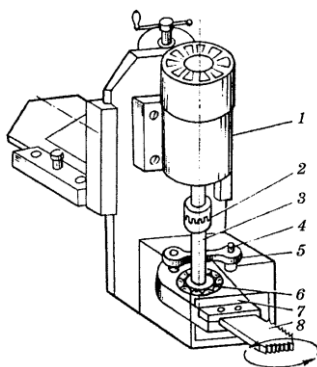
Головка довбального верстата: 1 – електродвигун; 2 – муфта; 3 – вал; 4 – вісь; 5 – тяга; 6 – ексцентрик; 7 – коромисло; 8 – фреза
